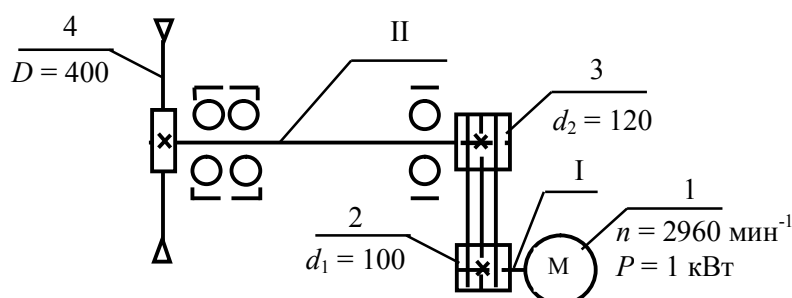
Кинематическая схема механизма главного движения круглопильного станка
